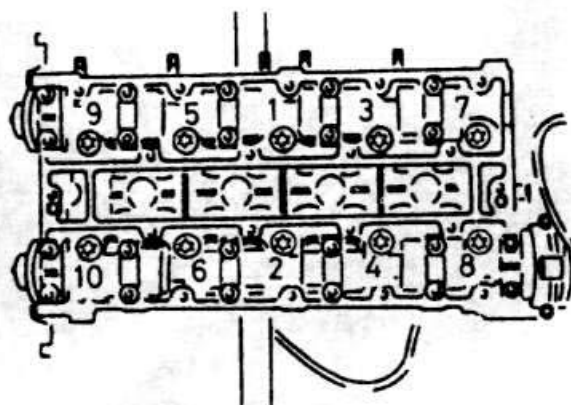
Последовательность затягивания болтов головки блока цилиндров — двигатель с двумя распредвалами
